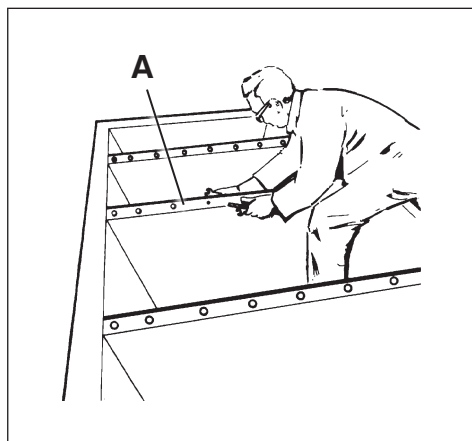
Fissare insieme gli assemblaggi con più tramogge
